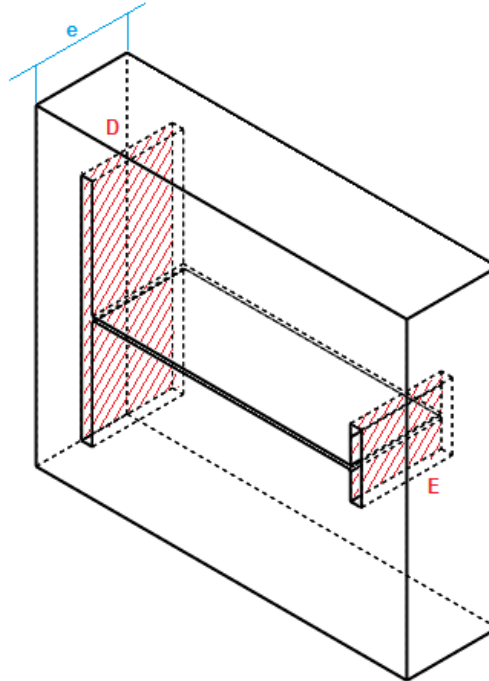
Planos de aplastamiento D y E para cuchilla fija
